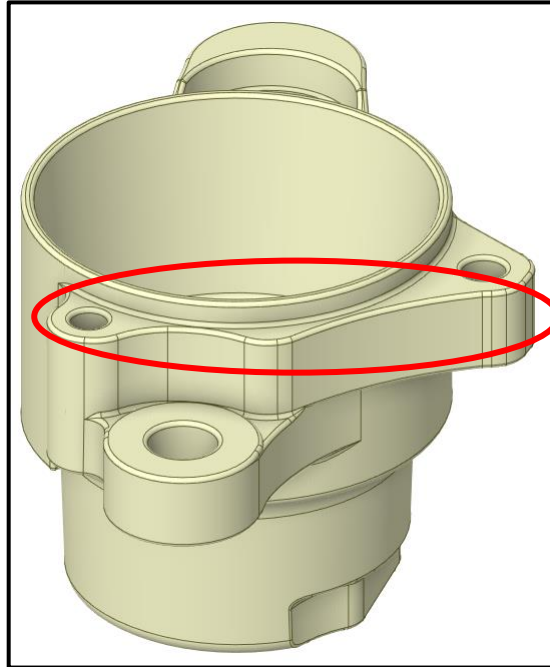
Návrh konstrukčního řešení č. 1 - Detail vnitřní hrany HO
